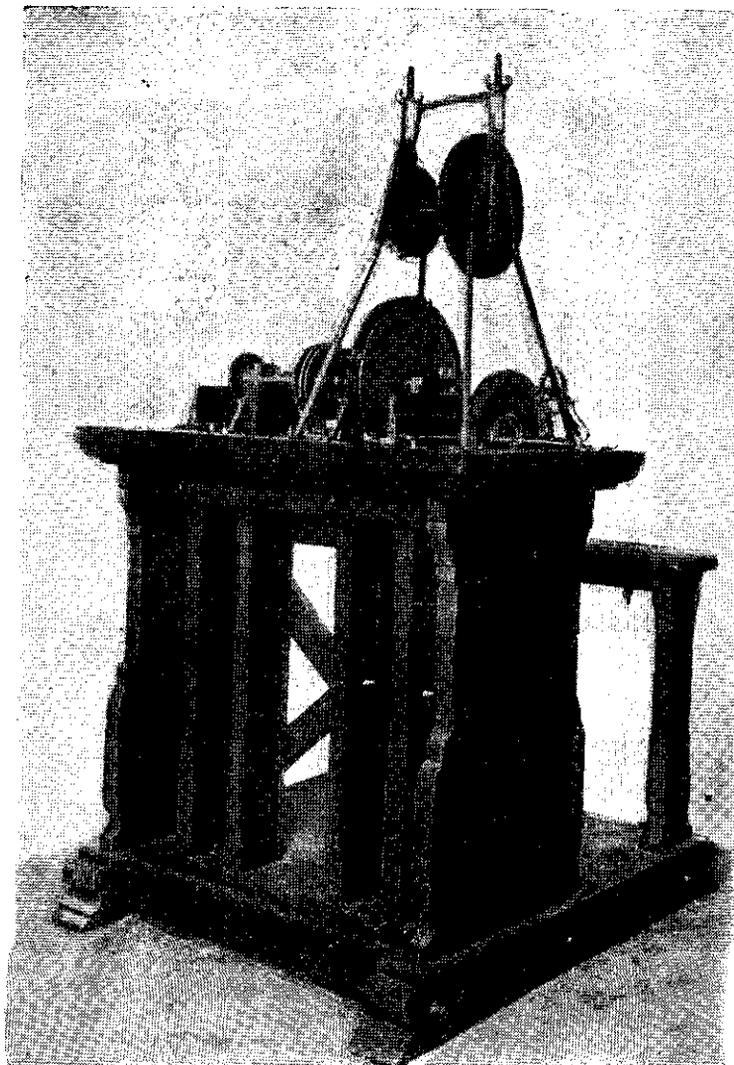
Медальерный токарно-копировальный станок Зингера (общий вид).
